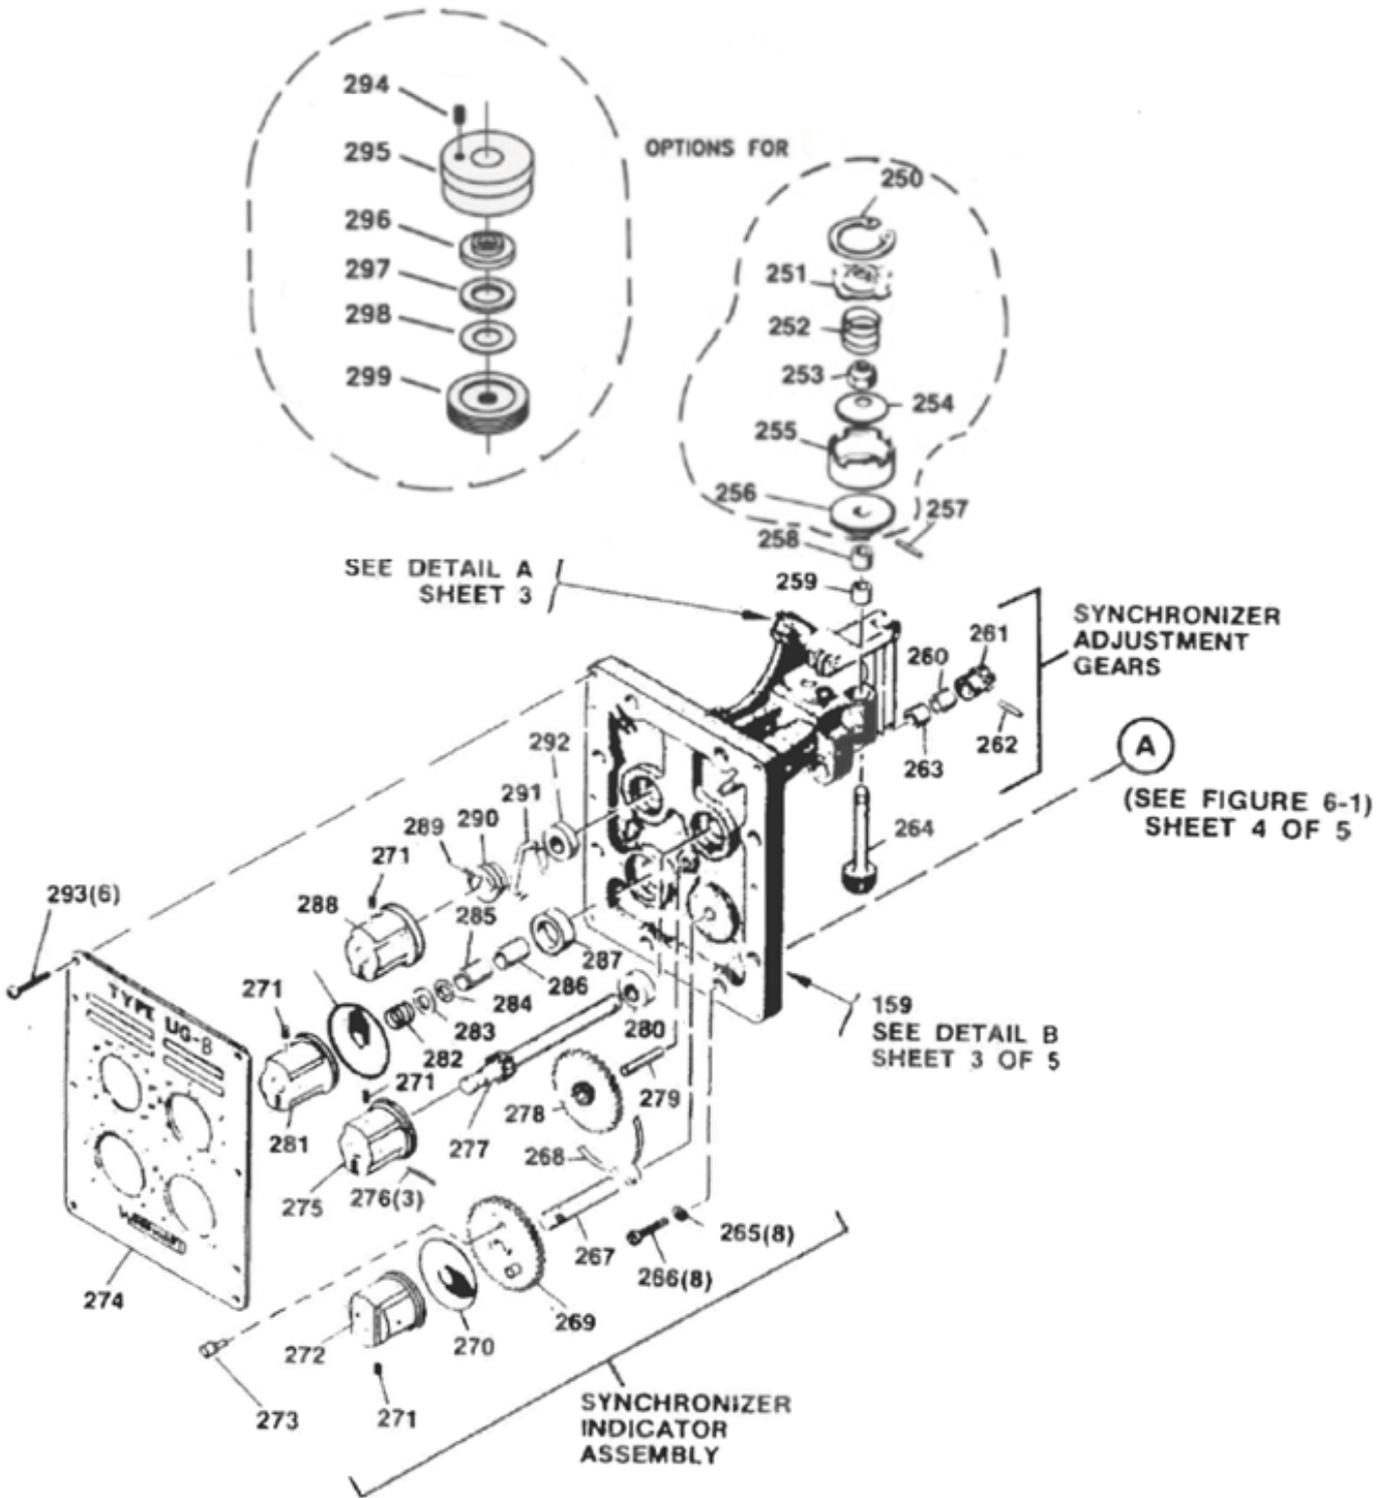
Illustration des pièces pour le régulateur à cadran UG
